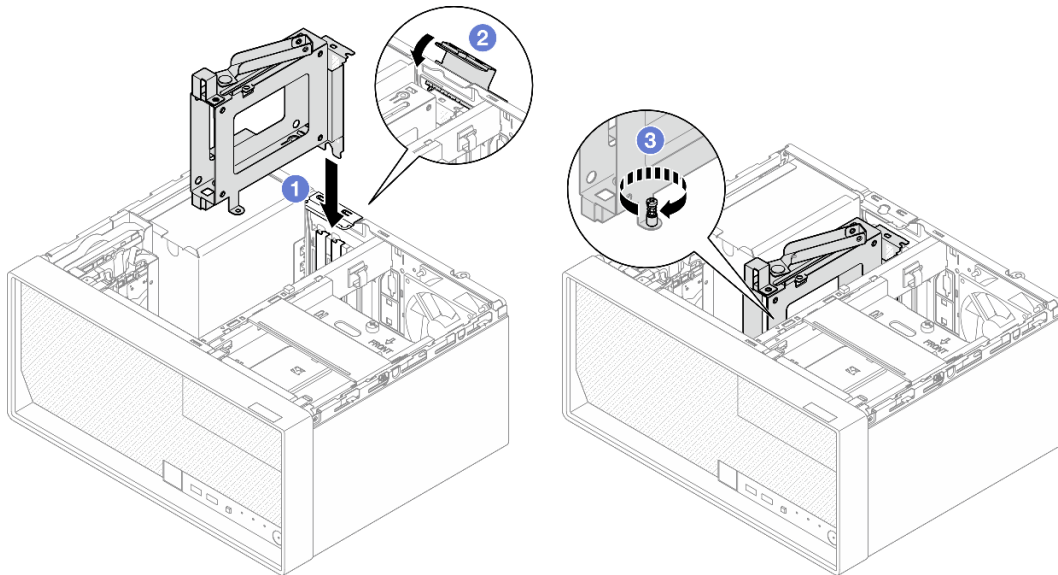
Installieren der Laufwerkhalterung in PCIe-Steckplatz 3
